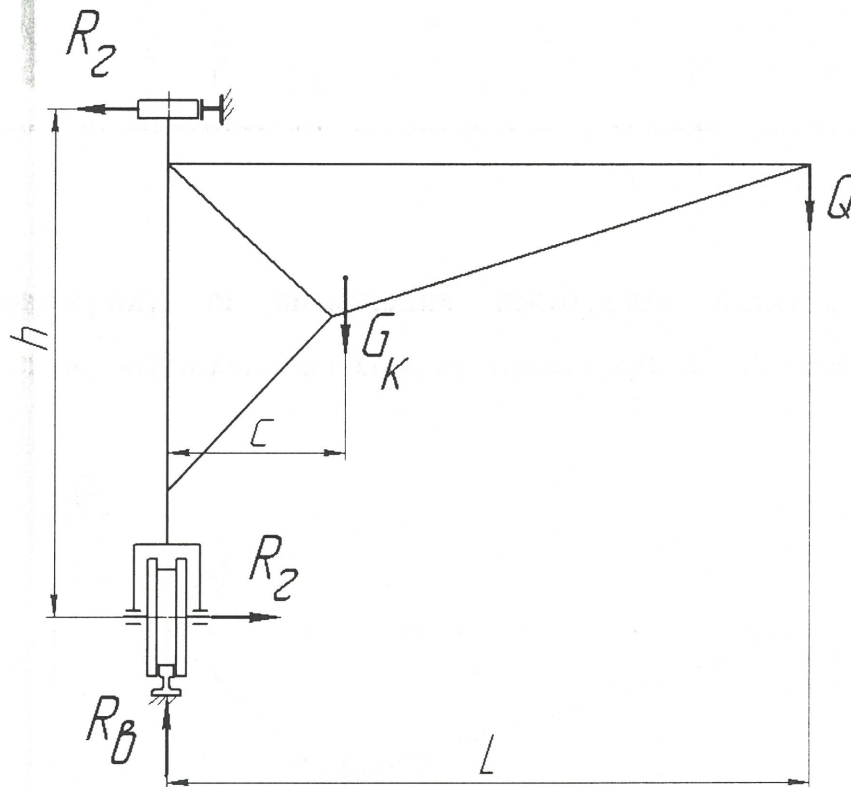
Схема до розрахунку навантажень на опори консольного крана
